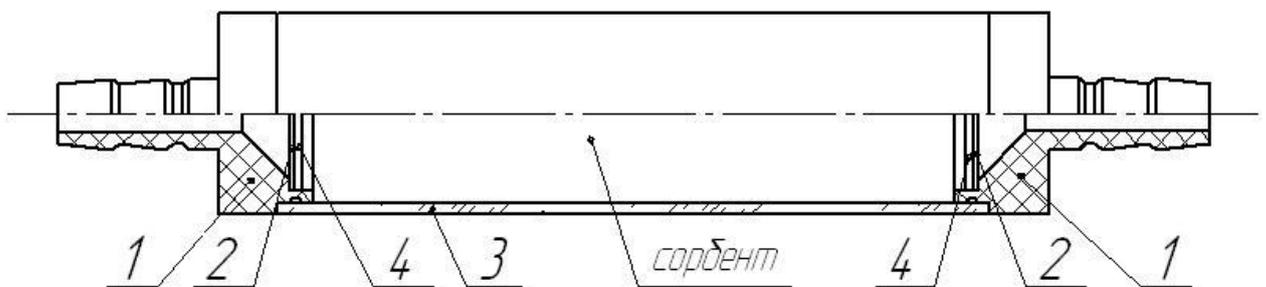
Внешний вид фильтра: 1- штуцер, 2- сетка защитная, 3- корпус фильтра, 4- кольцо стопорное.
